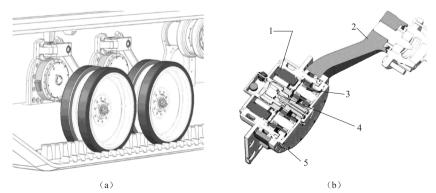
"枪骑兵"车轮站位置及 ECASS 作动器、平衡肘剖面 1—电动机; 2—平衡肘; 3—行星齿轮组; 4—传感器组; 5—平衡肘轴承
